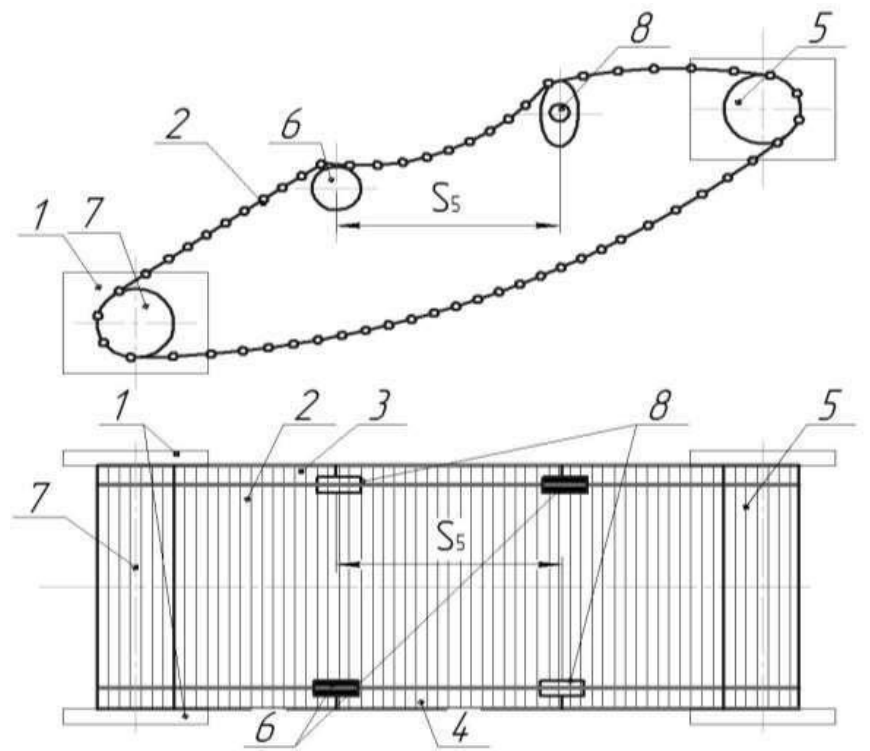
Схема пруткового елеватора з асиметричним розташуванням струшувачів машини для добору цибулі-сіянки: 1 – рама; 2 – елеватор прутковий; 3, 4 – гілки пруткового елеватора; 5 – ролики ведучі; 6 – ролики підтримувальні; 7 – ролики ведені; 8 – еліптичні струшувачі.
